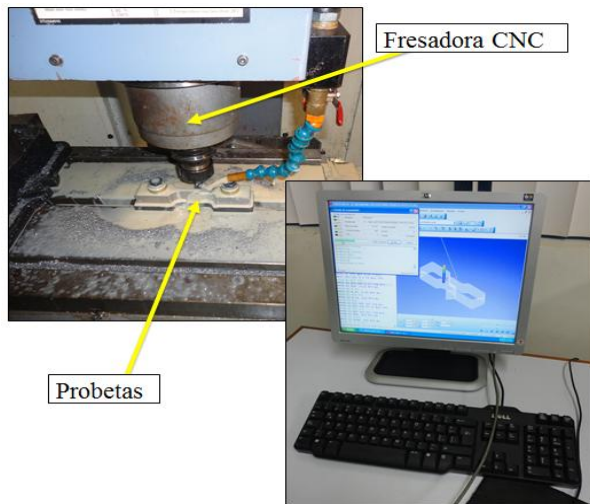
Proceso de maquinado en frío con Fresadora CNC (Control Numérico por Computadora)
